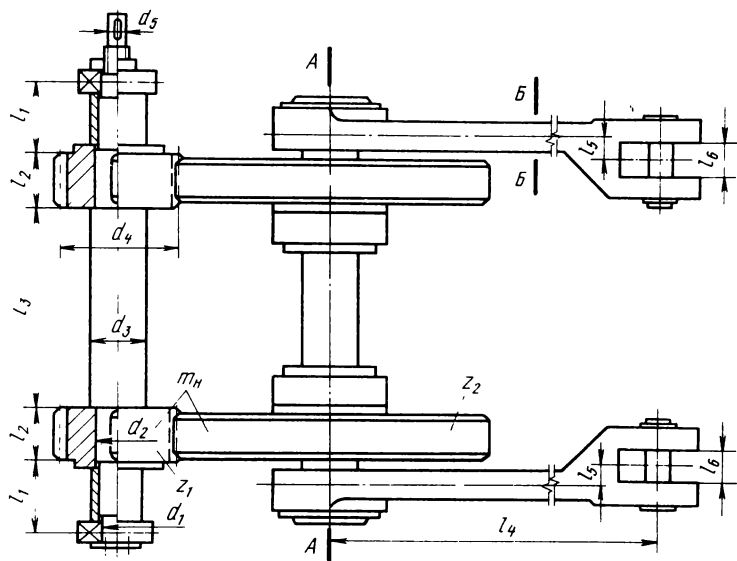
Узел ведущих и кривошипных зубчатых колес
